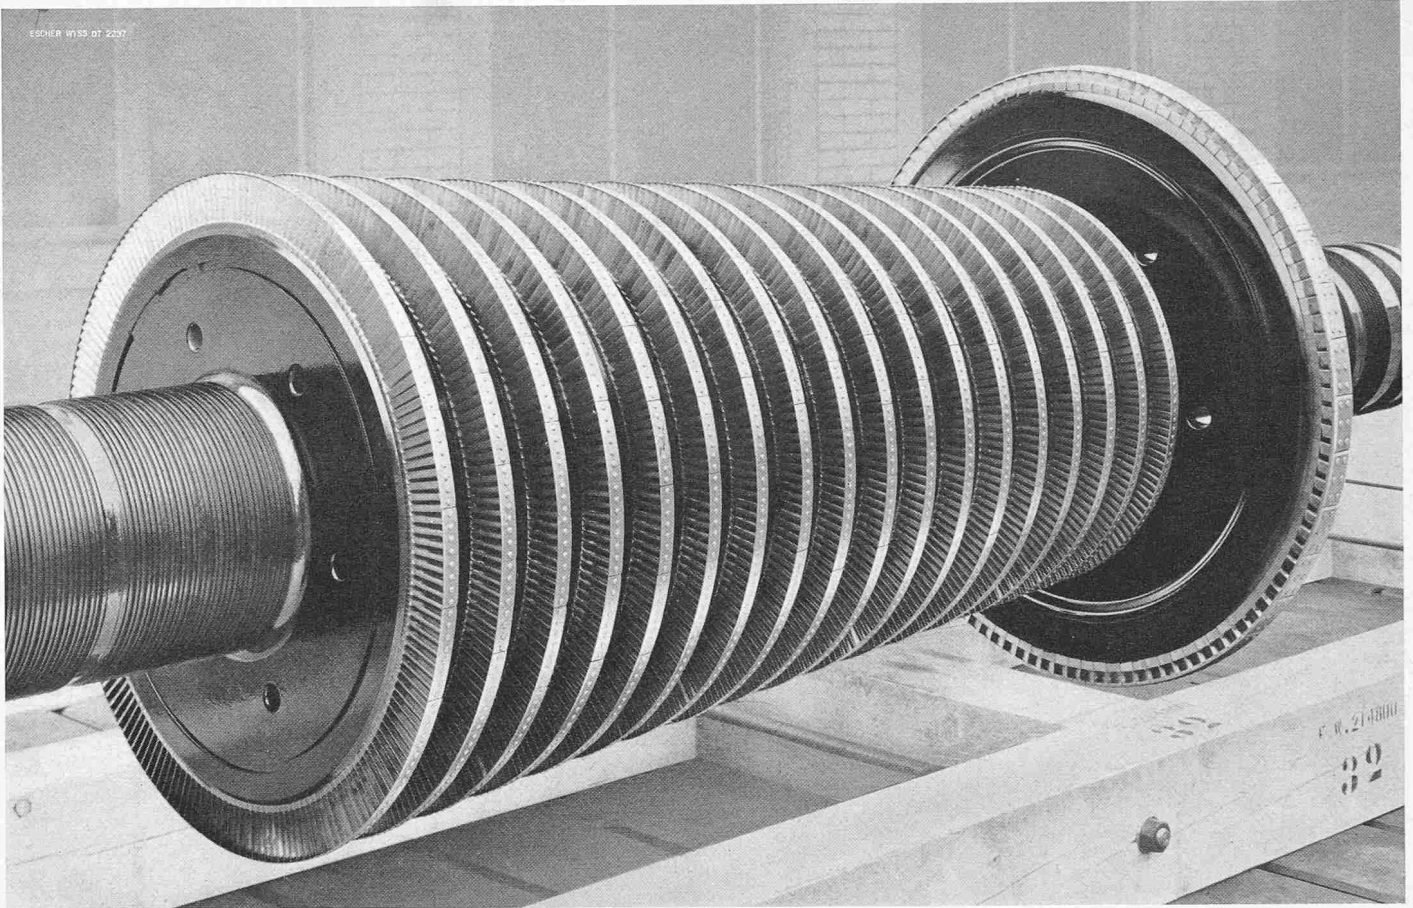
Hochdruck-Rotor mit grossem Regelrad am Eintritt und 18 Gleichdruckstufen. Der Rotor besteht aus einem Stück aus 12 % Chromstahl mit Zusätzen. In den Scheiben sind Nuten zum Einsetzen der Balanciergewichte vorgesehen
